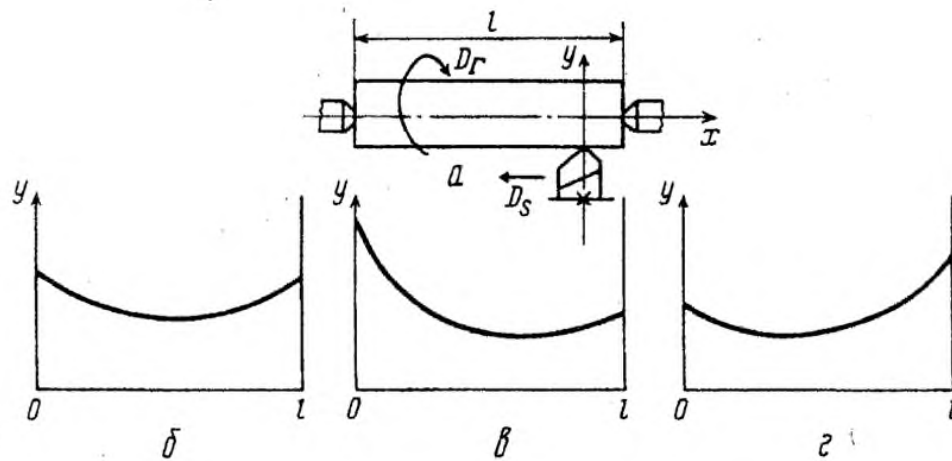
Схема обтачивания заготовок (а) и графики упругих деформаций при различных соотношениях жесткостей элементов токарного станка (б-г) [2]
